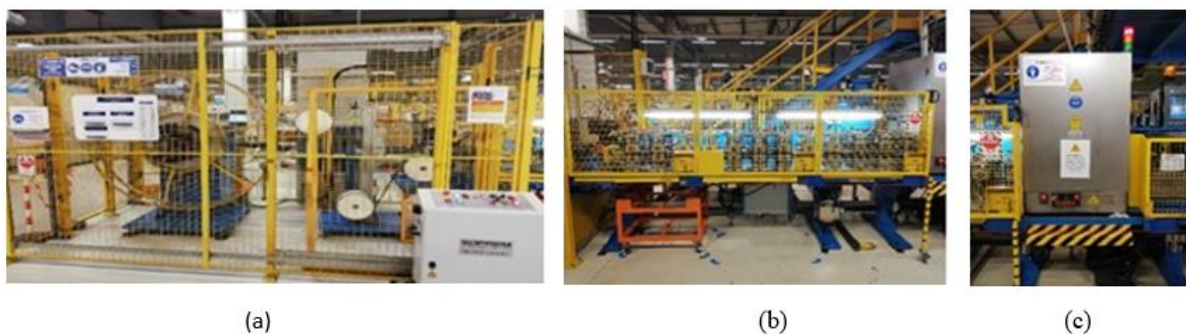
(a) Desbobinador e Acumulador, (b) Zona do Conformado, (c) Câmara de Soldadura
